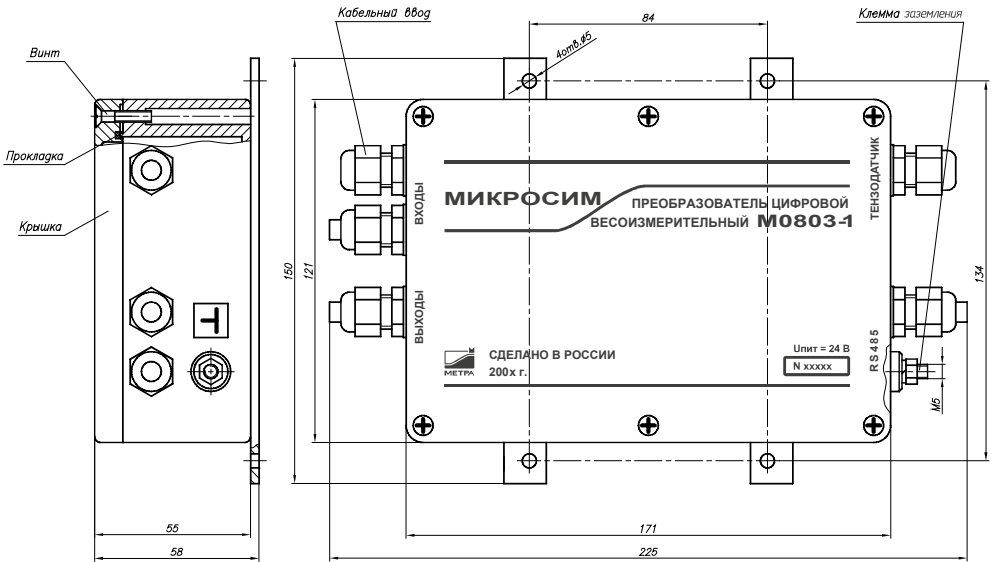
Внешний вид, габаритные и присоединительные размеры преобразователя
